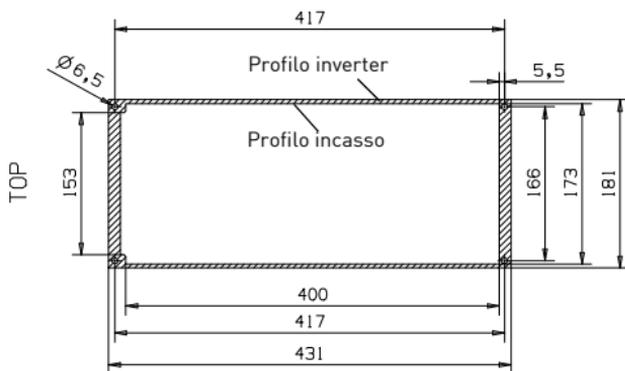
Misure dell'incasso per il montaggio a flangia per M15 (Unità: mm)
